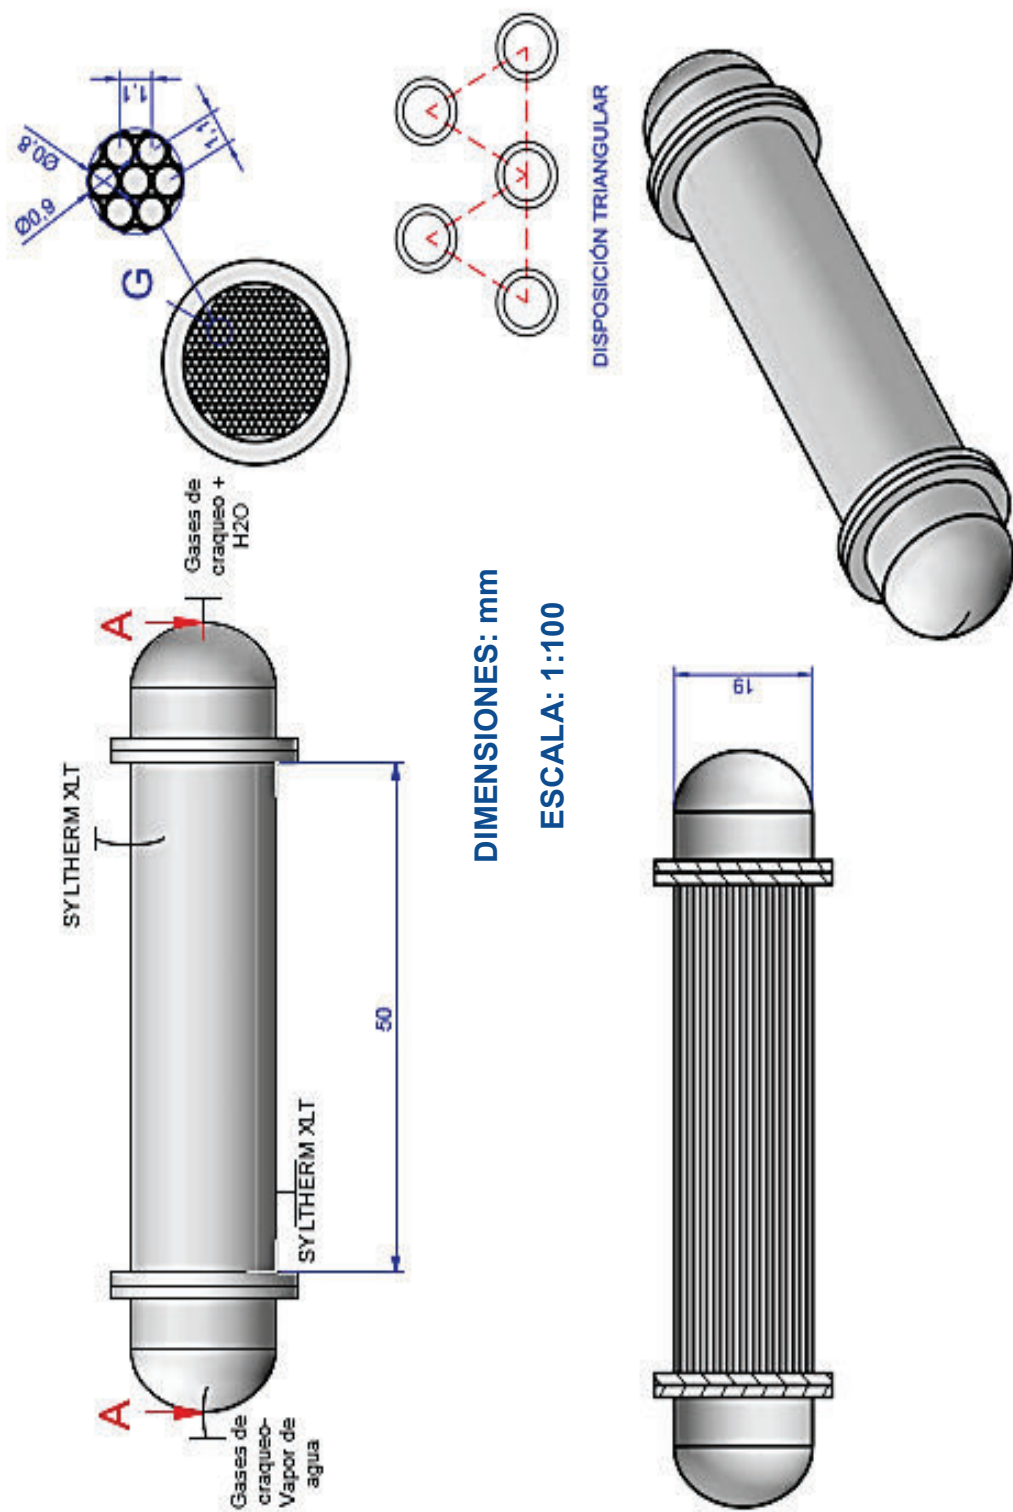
Dimensiones del intercambiador de calor 4 de tubos y coraza (E-103/E-104)
